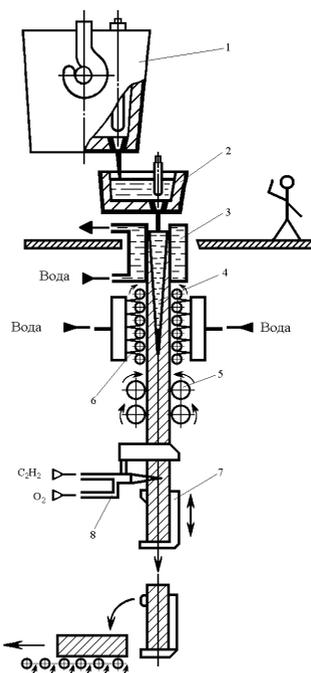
Схема разливки стали на машинах непрерывного литья:
